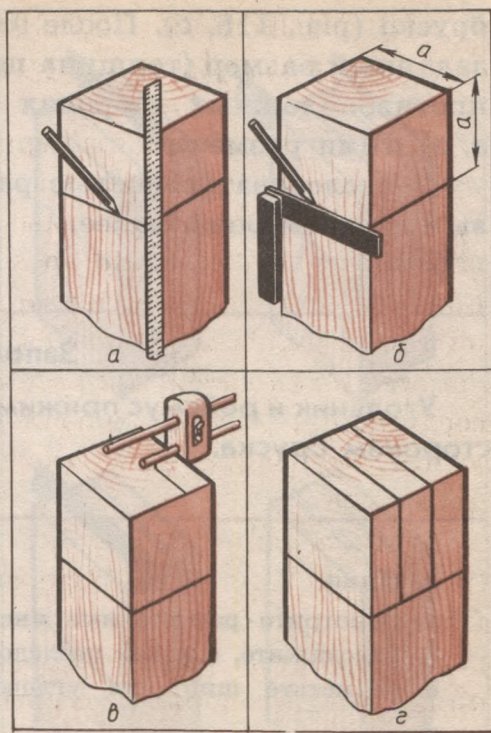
Разметка шипа: а — откладывание длины шипа по линейке; б — нанесение линии разметки по угольнику; в, г — разметка толщины шипа рейсмусом.
